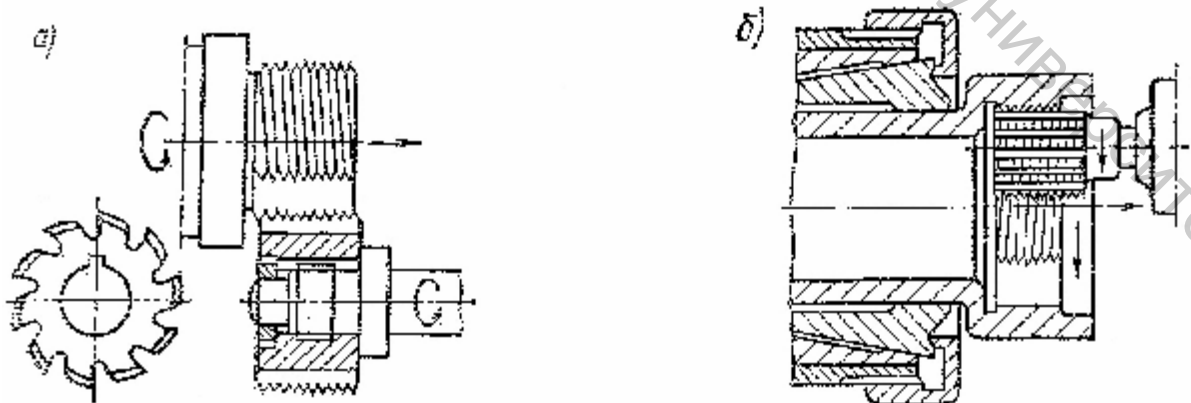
Схема фрезерования гребенчатыми фрезами
